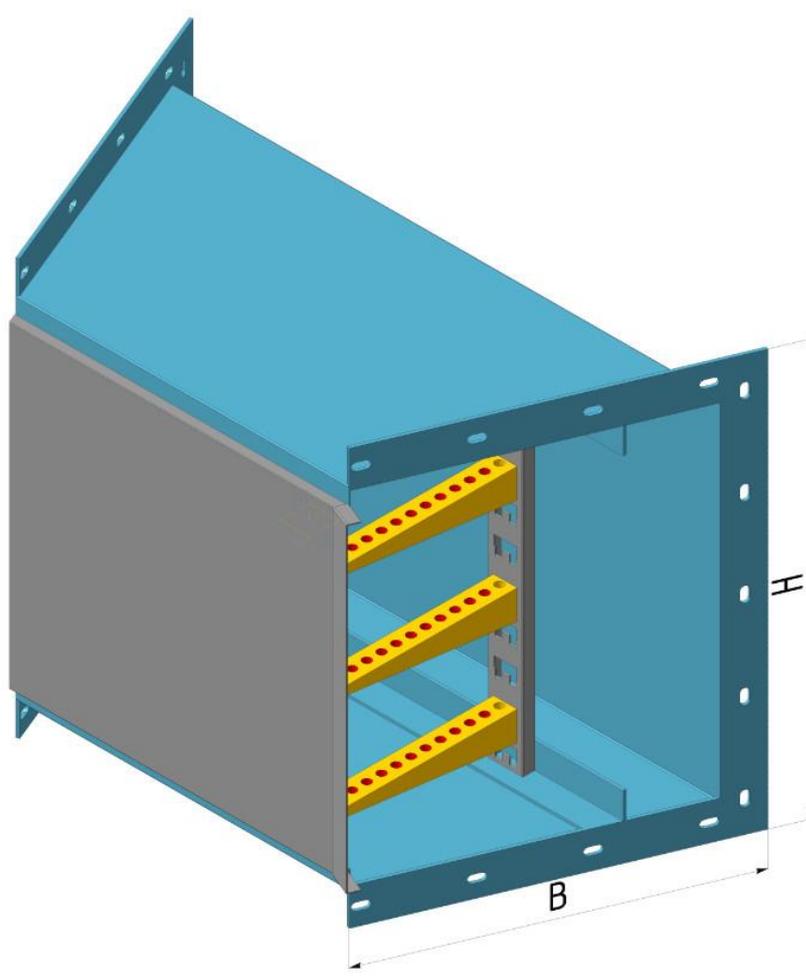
Короб кабельный блочный с внутренним углом поворота типа ККБ-УГВ. Общий вид
